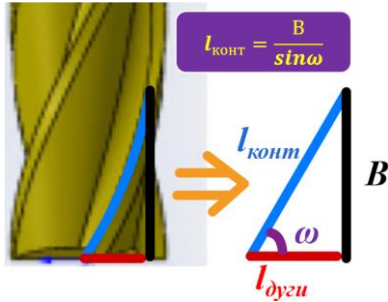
Схема, используемая для определения длины контакта режущей кромки с заготовкой при полном врезании зубьев фрезы в заготовку
